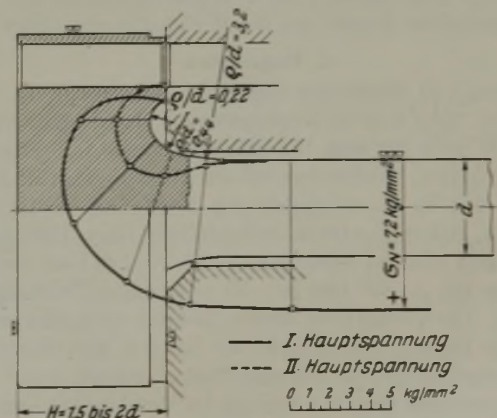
Kerbfreier Anschluß des Kopfes einer auf Zugdruck beanspruchten Zugstange unter Verwendung einer Exponentialkurve für die Hohlkehle.
